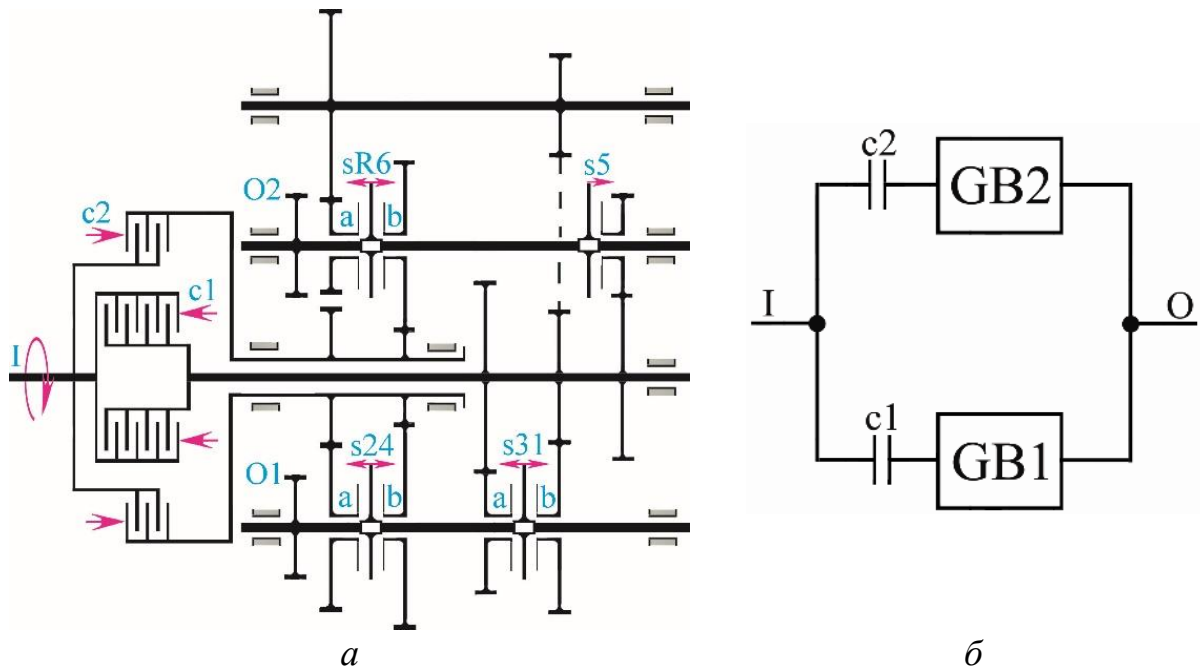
а – кинематическая схема 6-ти ступенчатой коробки передач с двумя сцеплениями; б – структурная схема коробки передач с двумя сцеплениями.
